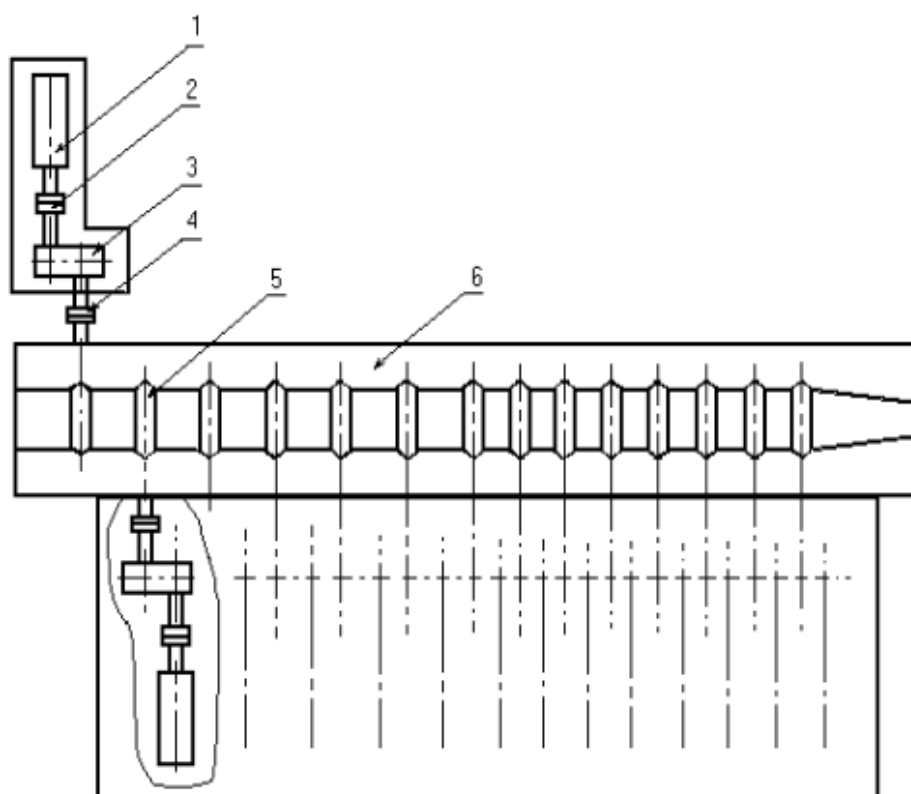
Общий вид рольганга: 1 – электродвигатель; 2,4 – зубчатая муфта; 3 – цилиндрический редуктор; 5 – ролик; 6 – рама рольганга
